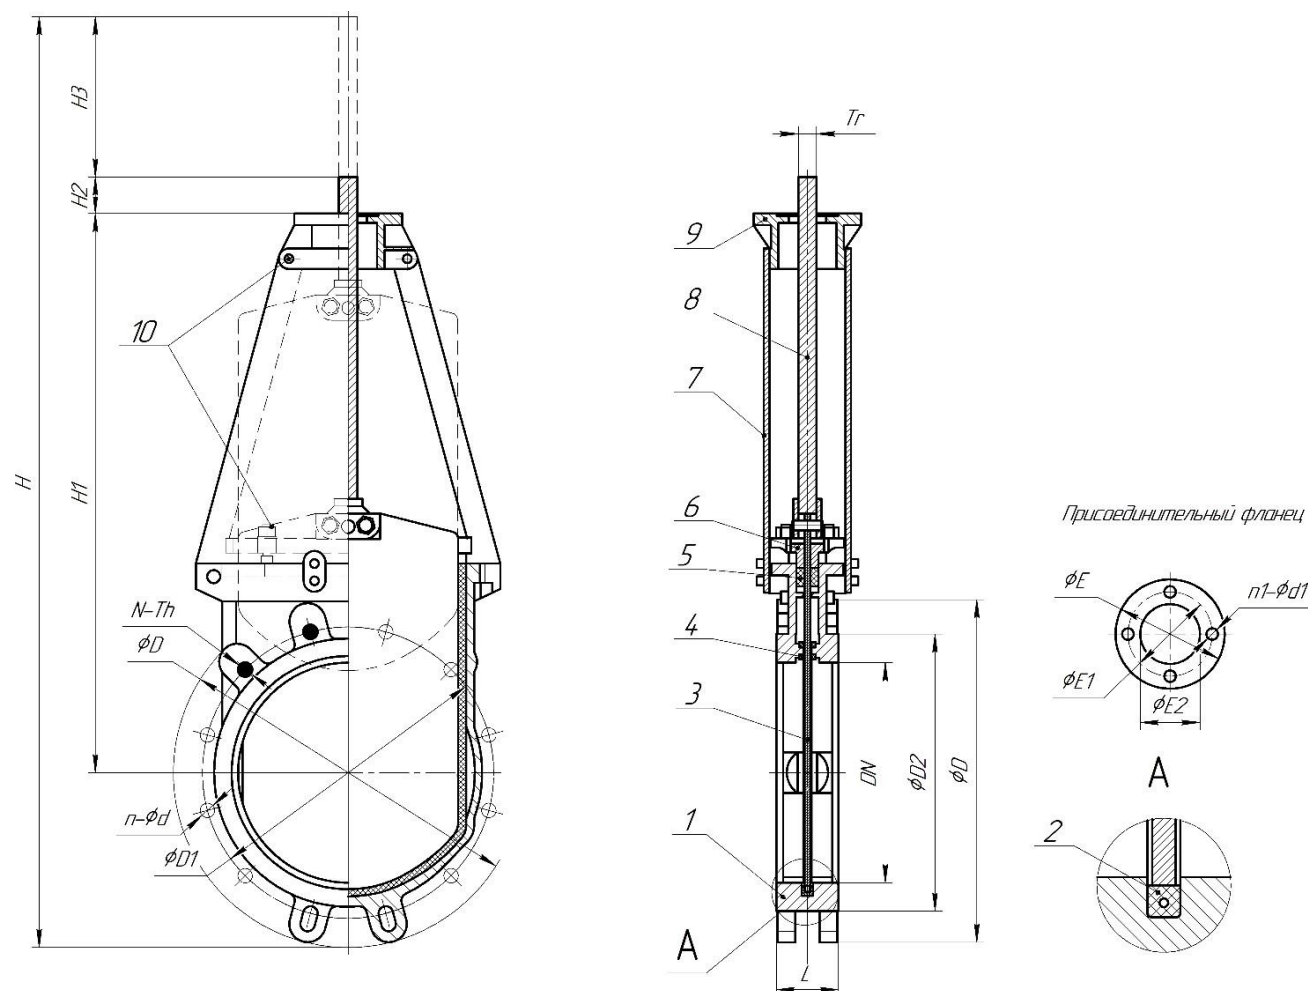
Задвижка без исполнительного механизма с выдвижным шпинделем DN50-1000
